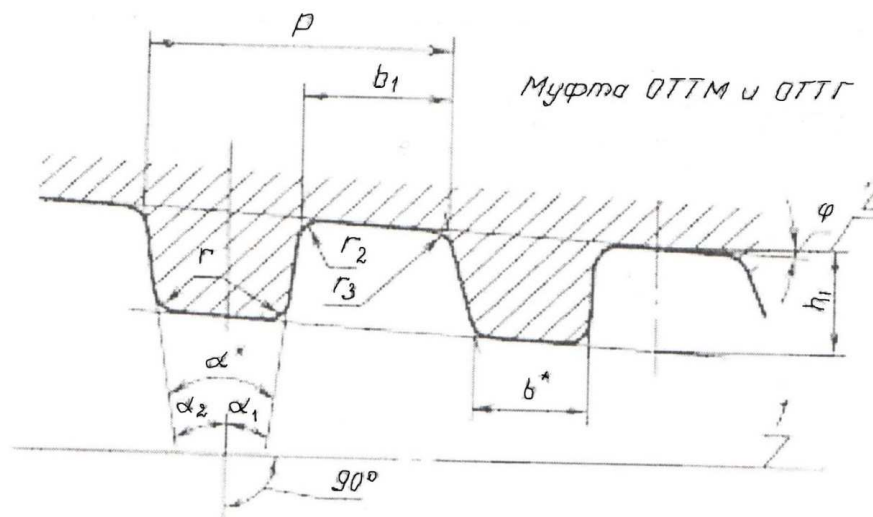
Вид резьбового соединения муфты с трапецидальной резьбой ОТТМ
